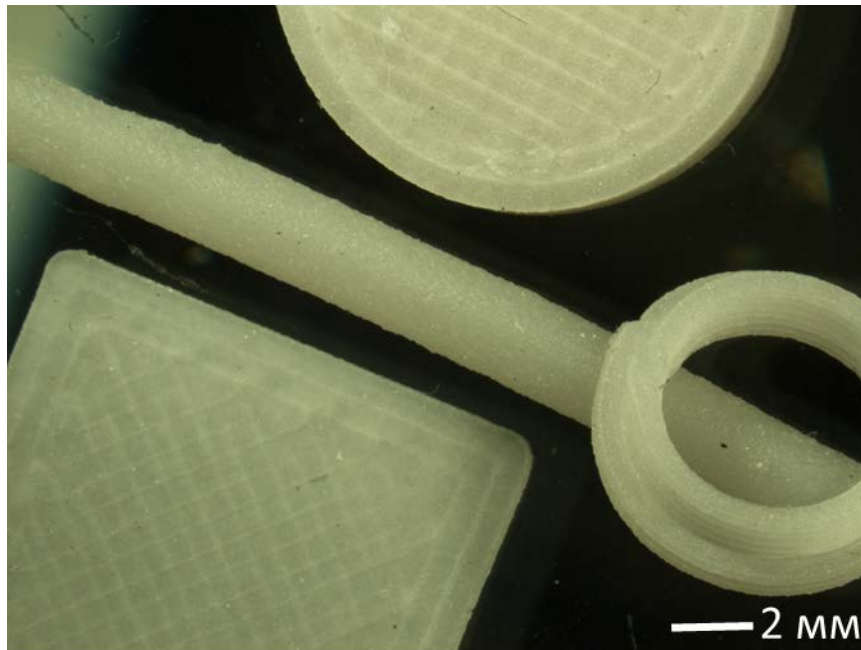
Стеклополимерный филамент и напечатанные из него изделия
